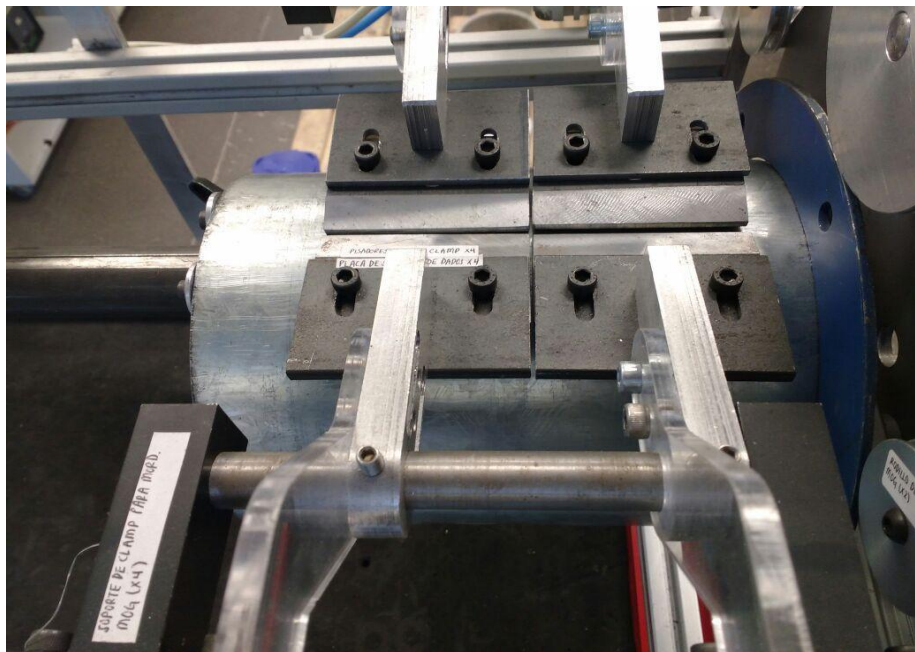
Se muestra el sistema de sujeción con las mordazas para la soldadura lineal
